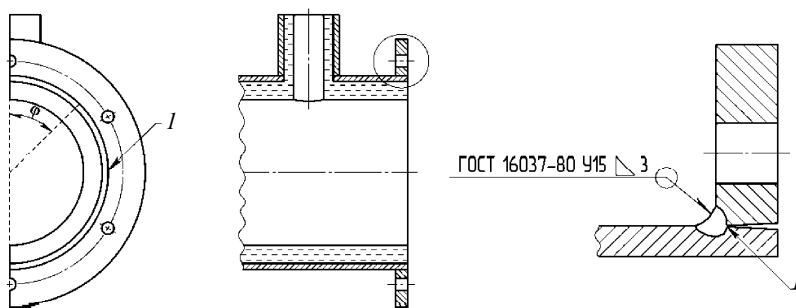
Схема сварного присоединения опорного фланца к обечайке с кольцевой технологической трещиной
